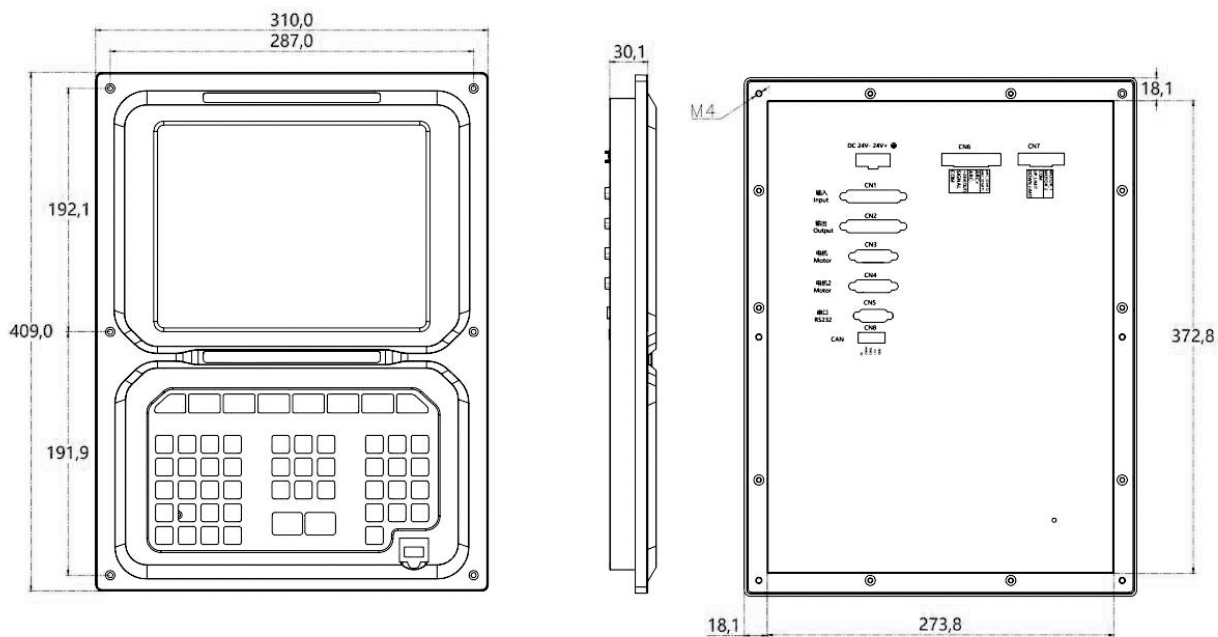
Установочные размеры ЧПУ контроллера FX430B.
